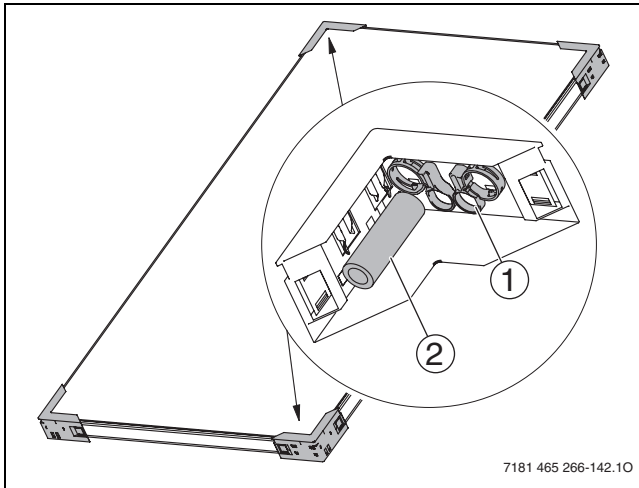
Два транспортировочных уголка с соединительными комплектами (здесь FKC-1)
